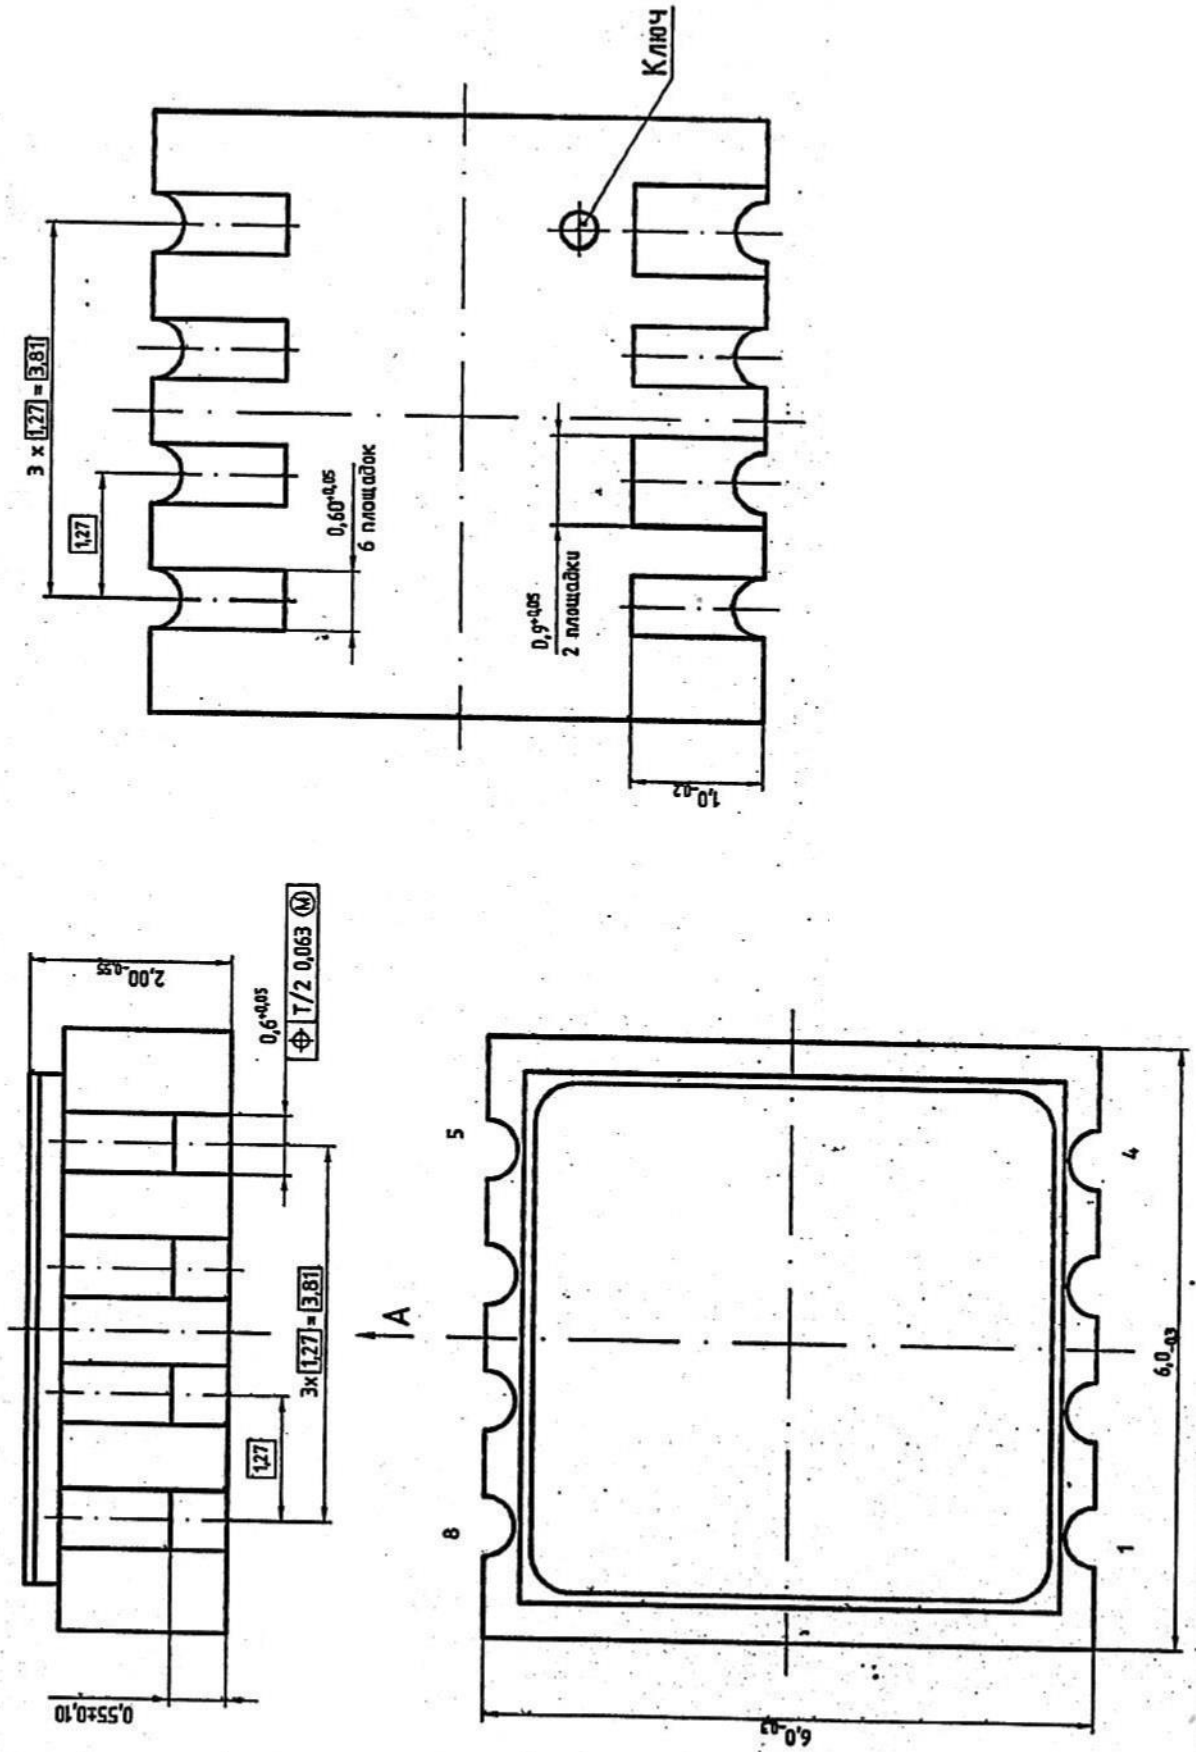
Габаритный чертеж корпуса 5205.8-2
